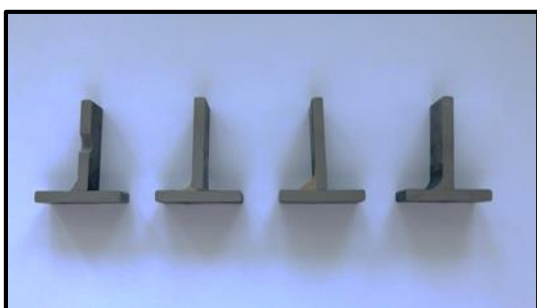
MIG – pájený spoj, Ø1 CuSi3
